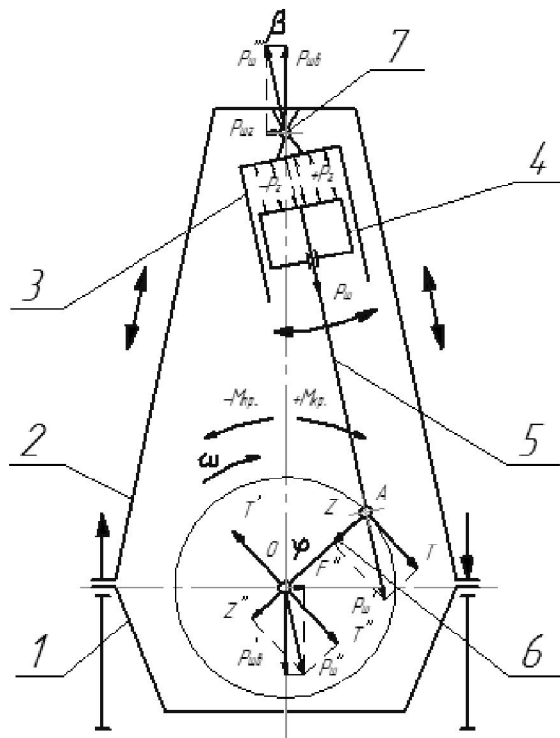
Поршковий двигун: 1 – фундаментна рама; 2 – станина; 3 – циліндр з кришкою; 4 – поршень; 5 – шатун; 6 – колінчастий вал; 7 – шарнір
